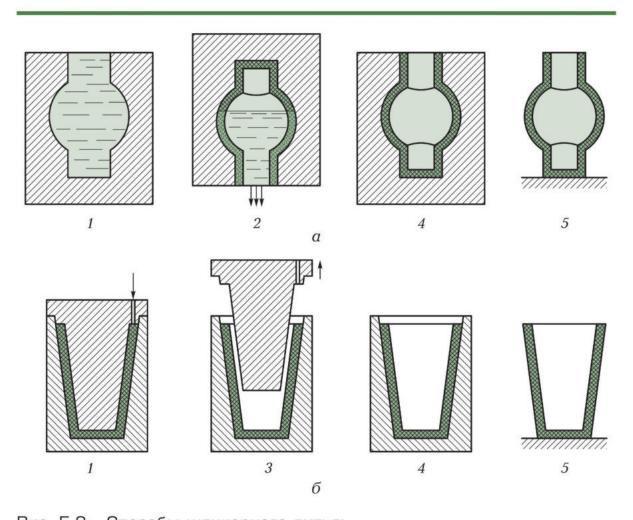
Способы шликерного литья: a — сливной; δ — наливной; 1 — заливка шликера; 2 — слив излишнего шликера; 3 — разъем формы; 4 — подвялка; 5 — отформованные изделия
